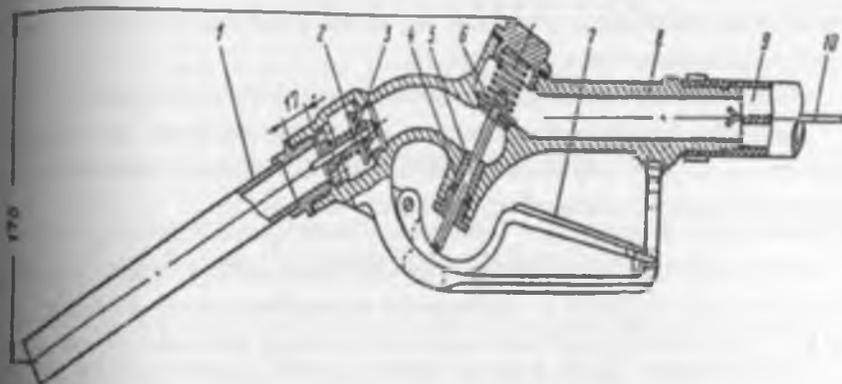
Разрез раздаточного крана: 1 — сливная труба; 2 — гайка отсечного клапана; 3 — отсечной клапан; 4 — сальник; 5 — шток; 6 — клапан с пружиной; 7 — рычаг; 8 — корпус; 9 — рукав; 10 — провод заземления
